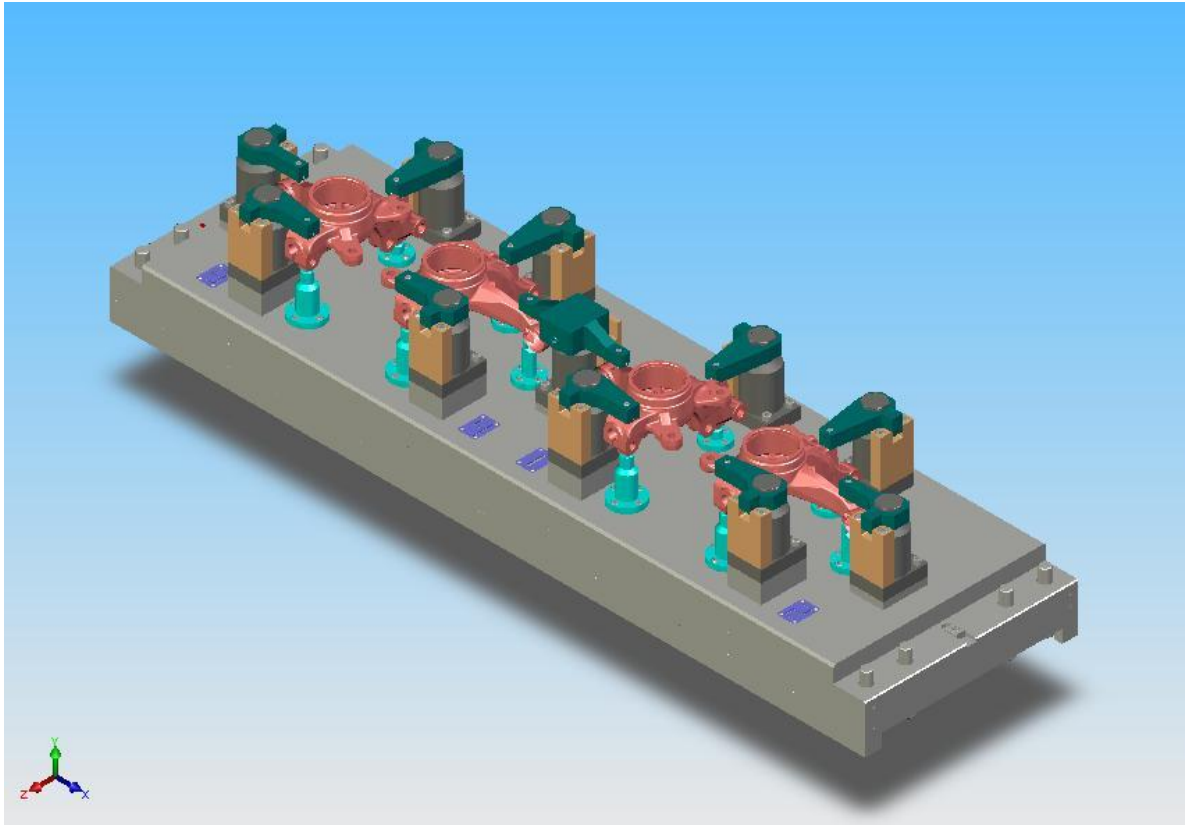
Desenho de Conjunto do Dispositivo Hidráulico
